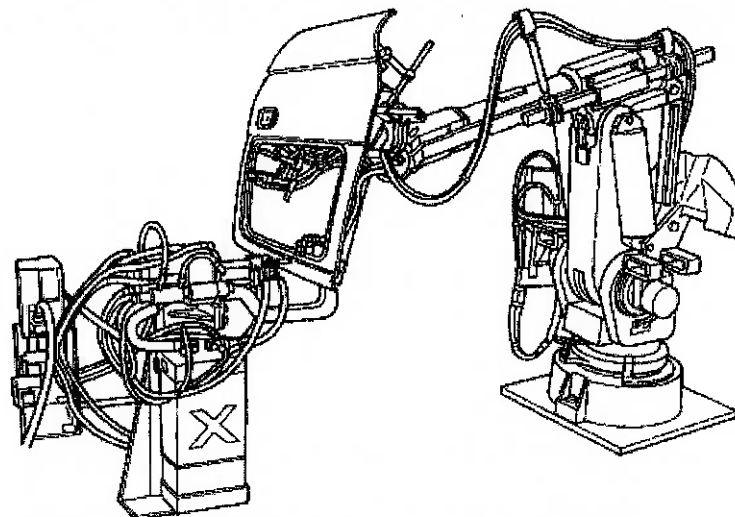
Pedestal para Máquina de Solda a Ponto
